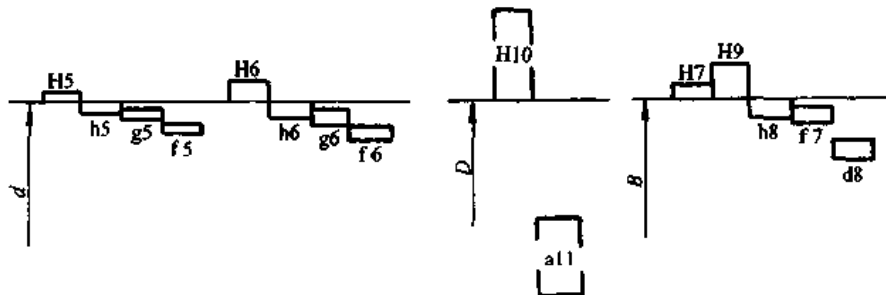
精密传动矩形花键的尺寸公差带
